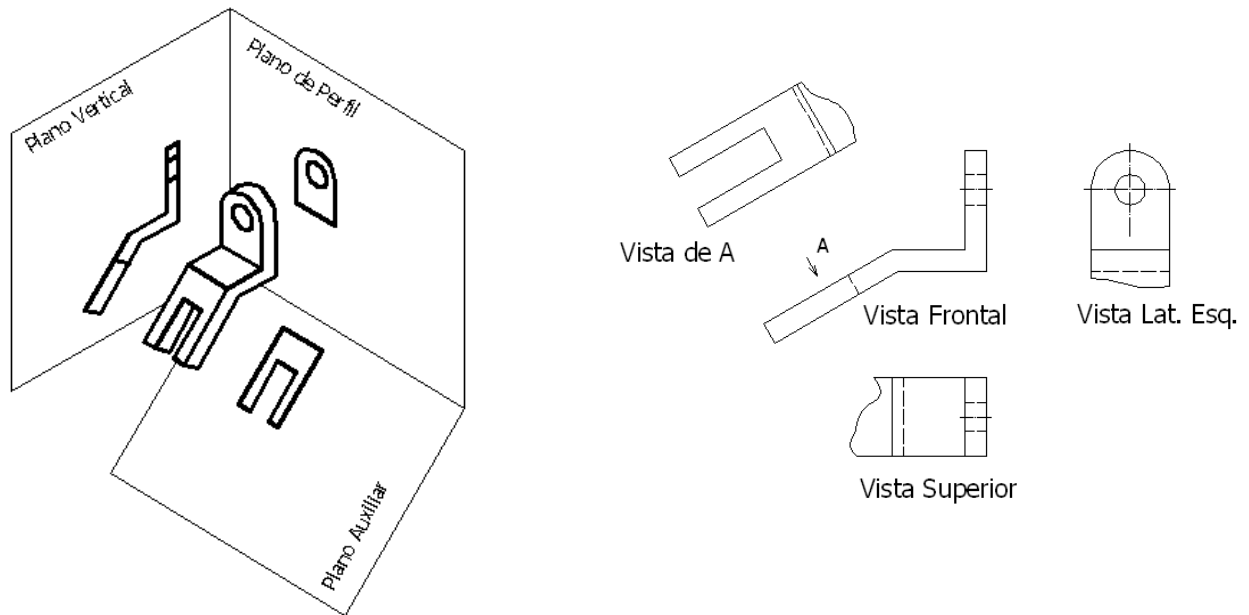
Vista auxiliar de um objeto para identificar a VG de sua superfície inclinada
